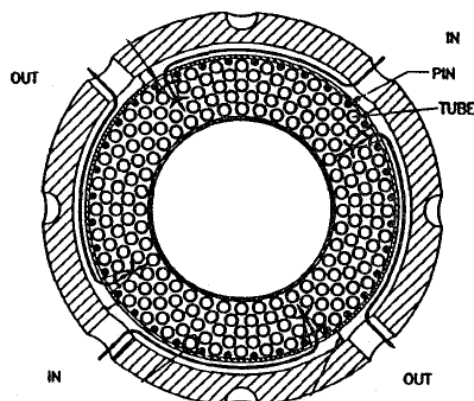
Corte de um permutador de calor tubular de um motor Stirling. [60]
